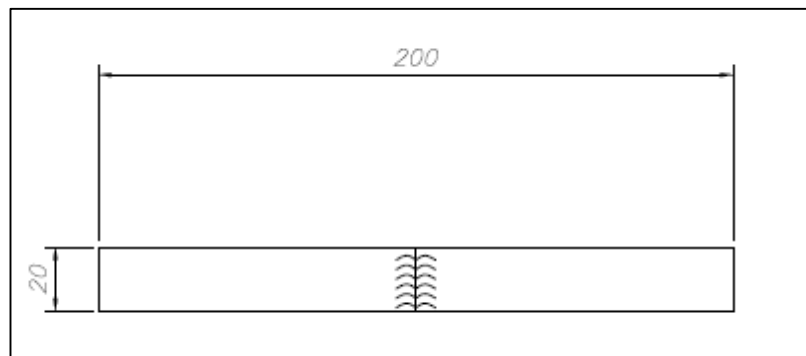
Dimensiones (en mm) de las probetas de uniones soldadas fabricadas.
